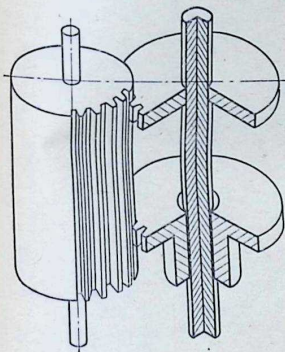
Схема прибора для измерения зубчатых колес с однопрофильным зацеплением.
